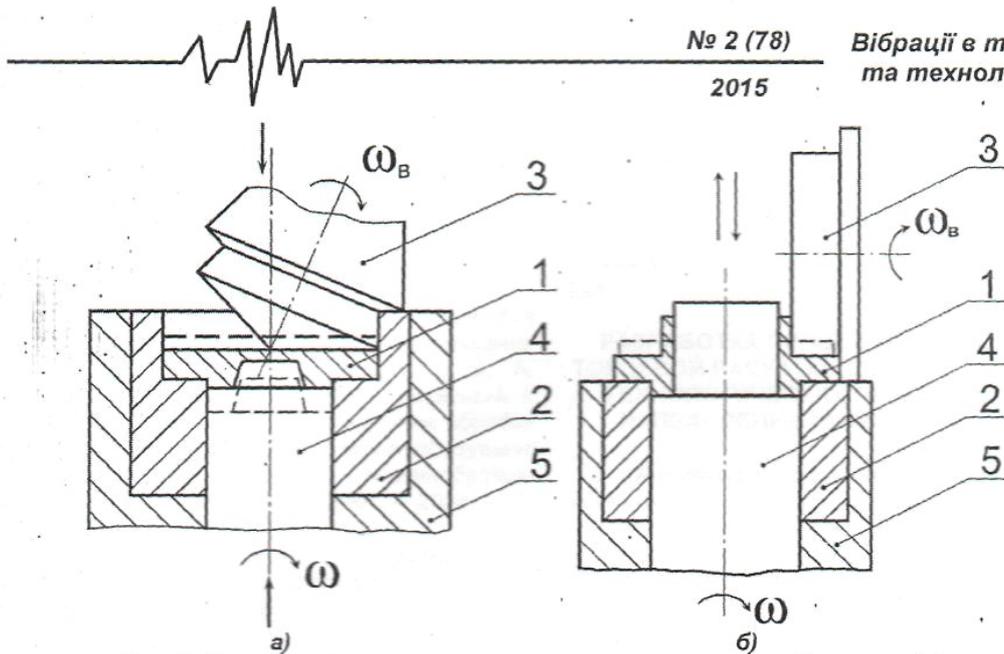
Послідовність виготовлення розкочуванням фланця з комірцем з використанням вихідної квадратної заготовки:
